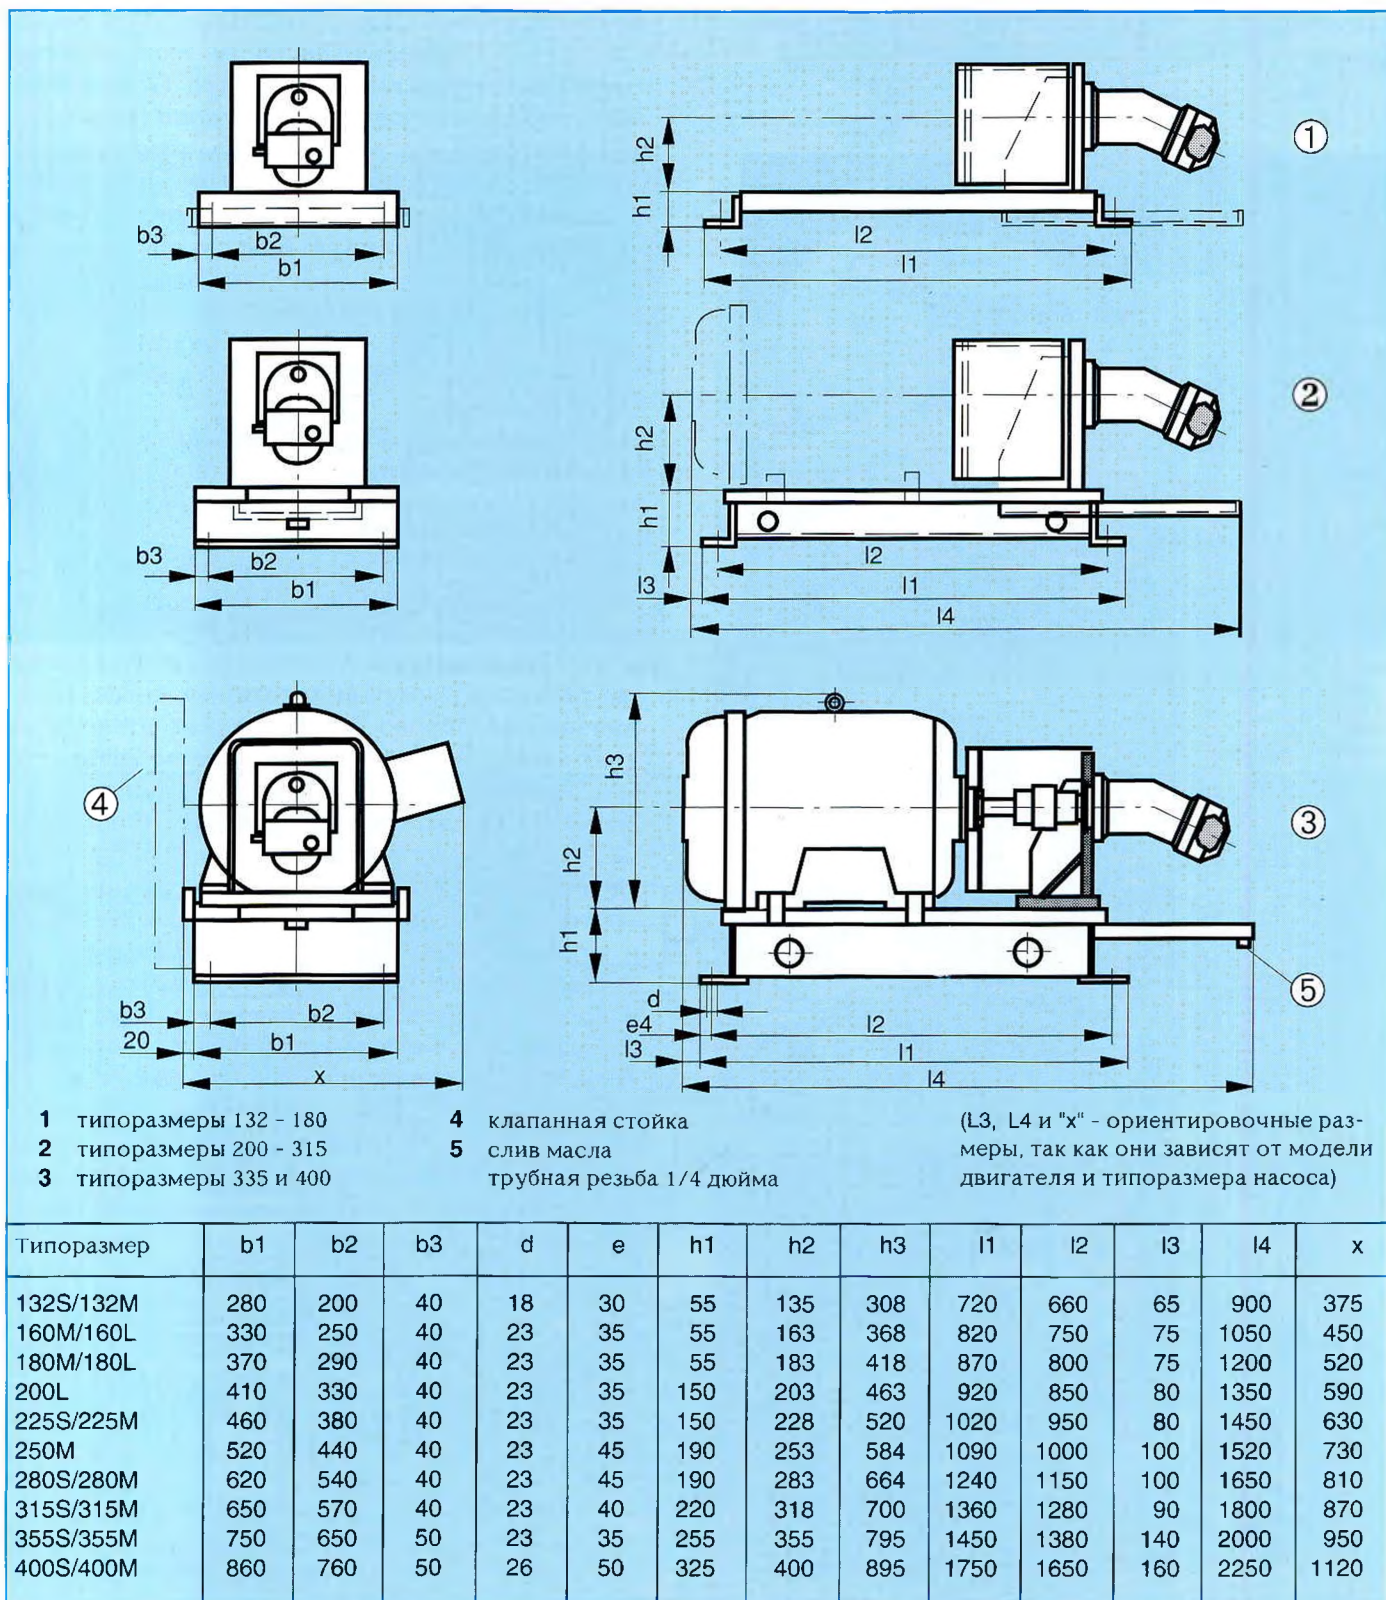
Основные размеры узла двигатель-насос с электродвигателем типа ВЗ
